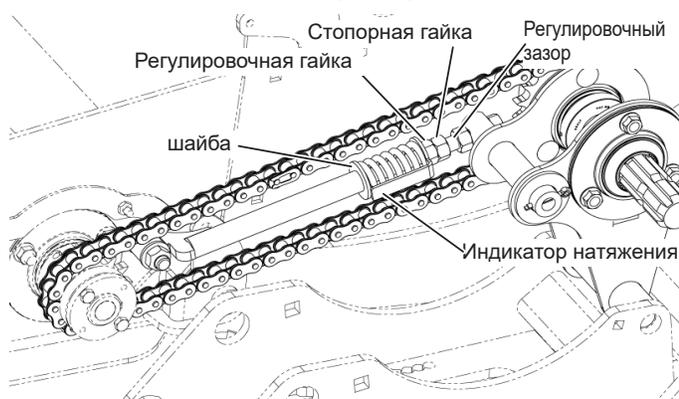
Регулировка натяжения приводной цепи центрального транспортера
